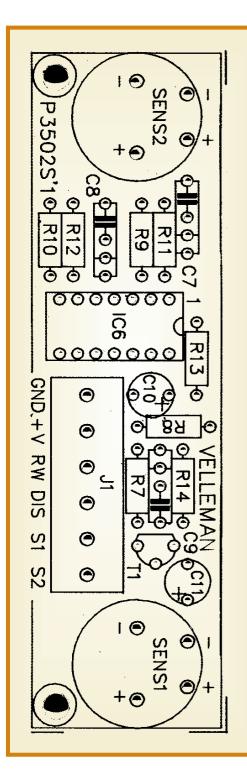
Lado del componente de la plaqueta del receptor.
